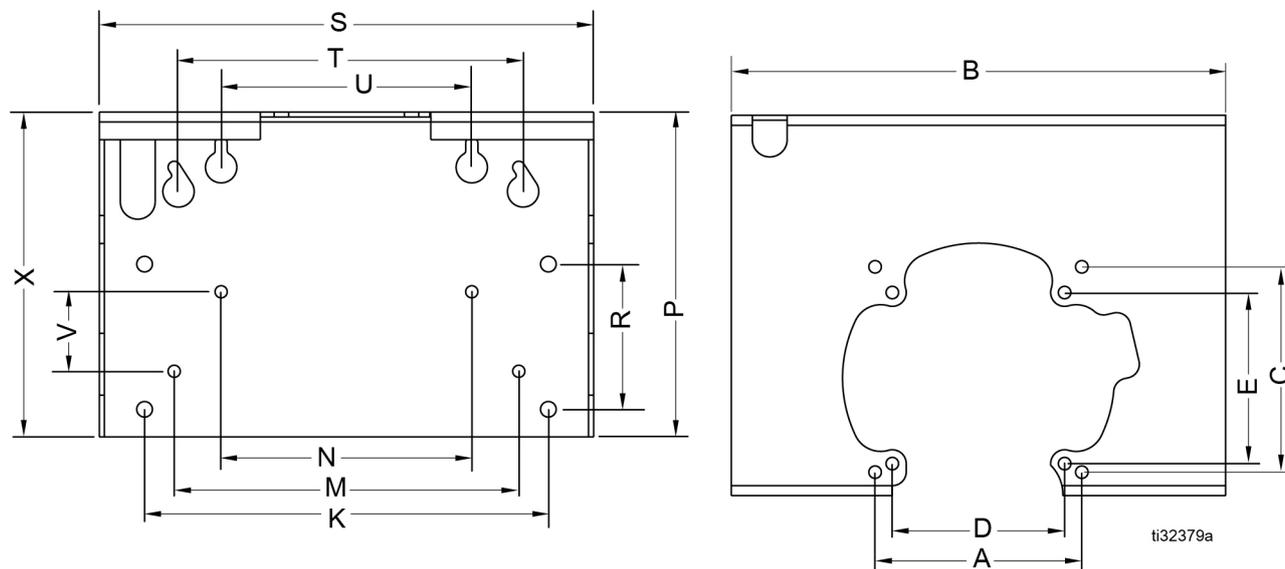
Dimensioni dei fori di montaggio a parete per pacchetti di spruzzatura e pompe King PC
